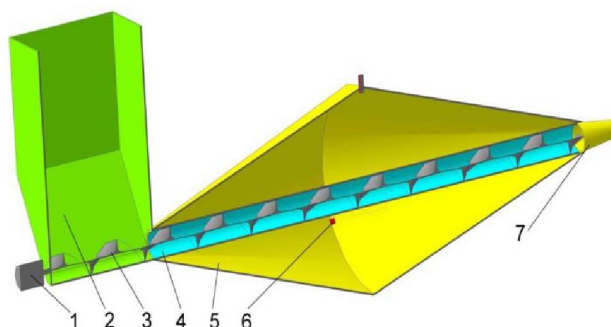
Сверхвысокочастотная установка с биконическим резонатором для термообработки и обеззараживания отходов животного происхождения: 1 – мотор-редуктор для привода диэлектрического шнека; 2 – загрузочная емкость для измельченного сырья; 3 – винтовой шнек; 4 – цилиндрический корпус шнека; 5 – биконический резонатор; 6 – магнетроны СВЧ генератора; 7 – выгрузное отверстие на вершине кругового конуса
